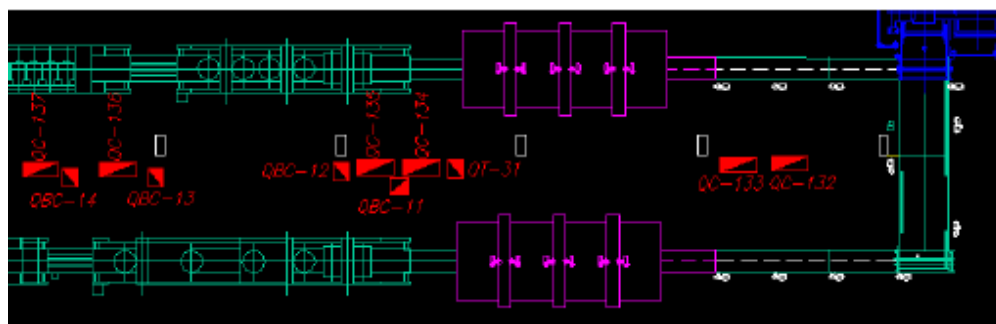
Layout da Elizabeth Revestimentos atualizado.
